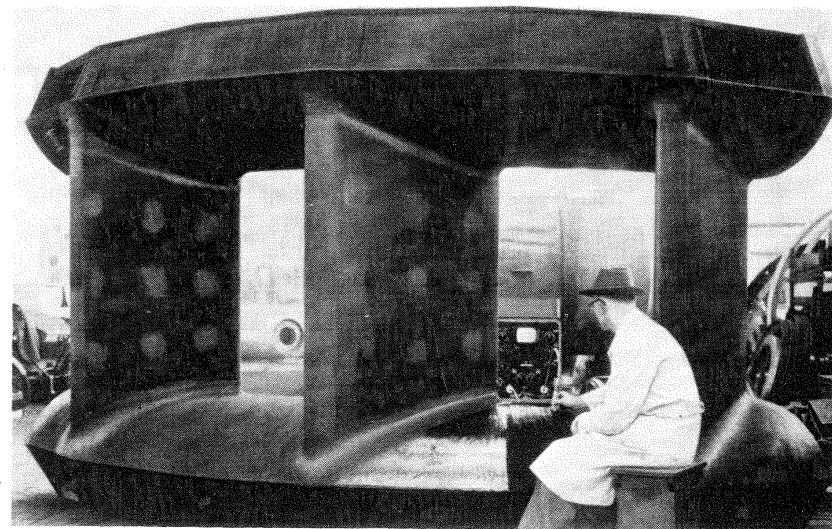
Prueba de la soldadura de un predistribuidor por ultrasonido.
